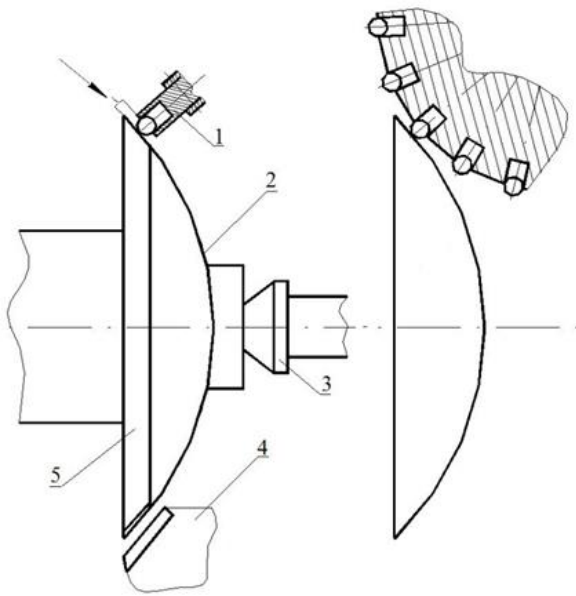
Схема обробки різальної кромки диска: 1 – ротаційна головка; 2 – диск борони; 3 – віджимний центр; 4 – різець, 5 – оправка
